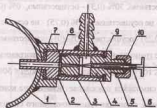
Схема беспоплавокго карбюратора для подачи метанола во впускной трубопровод: 1 - впускной трубопровод; 2 - корпус карбюратора; 3 - жиклер; 4 - корпус регулировочной иглы; 5 - гайка сальника регулировочной иглы; 6 - регулировочная игла; 7, 8, 9 - уплотнительные прокладки; 10 - сальник
